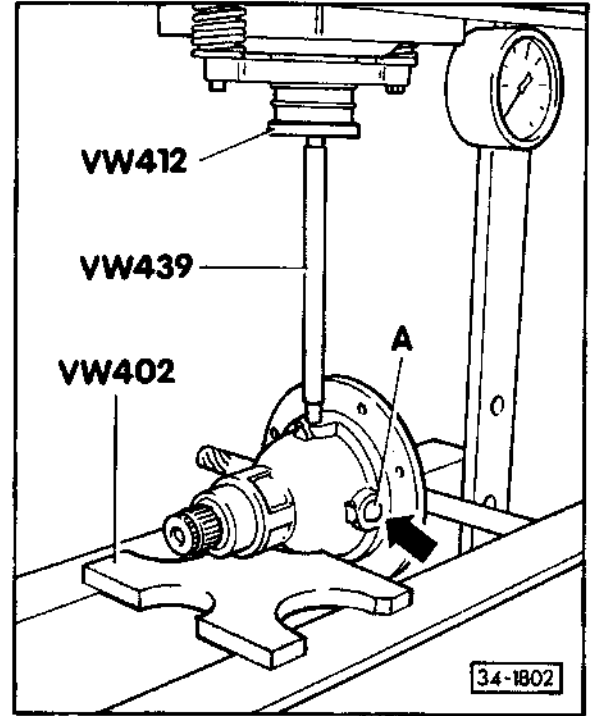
Achsen (kurz) für Ausgleichkegelräder auspressen
